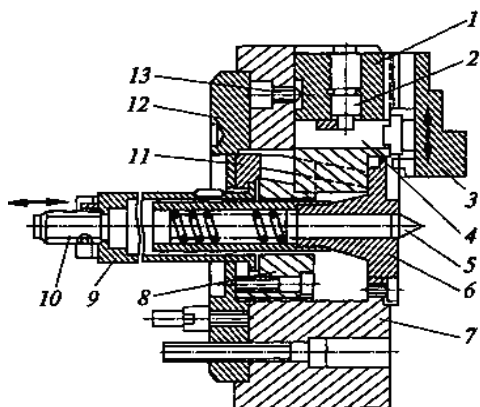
Самоцентрирующие трехкулачковые клиновые патроны для обработки заготовок типа вала.
